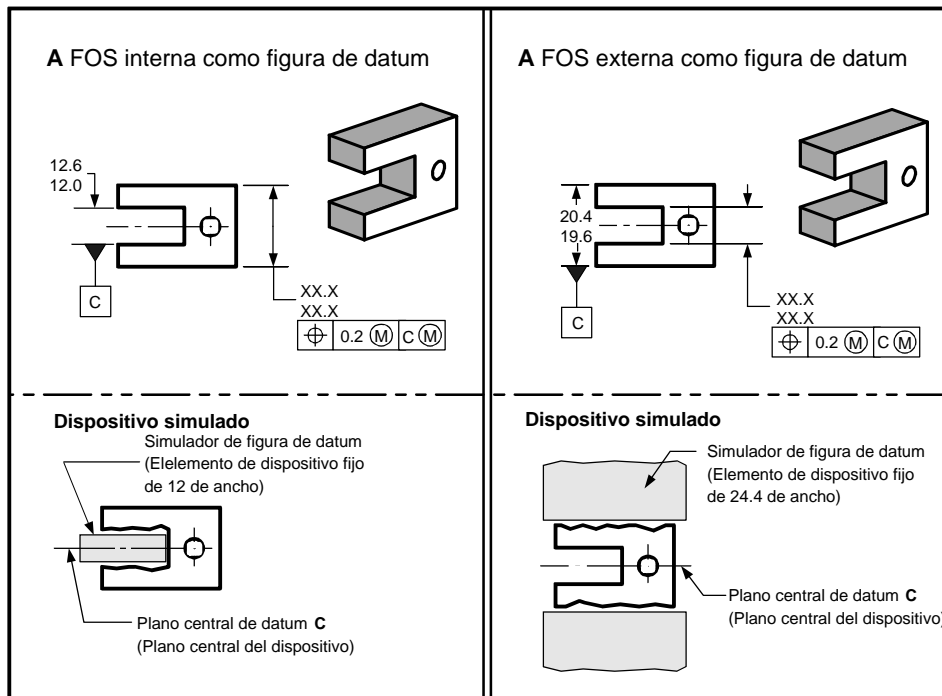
Datum de plano central a MMC primario
